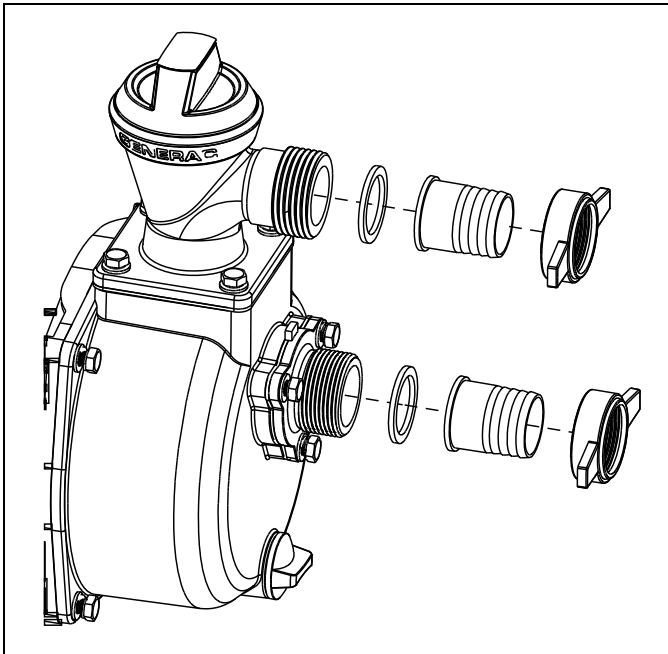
Fixation d'un joint et d'un raccord cannelé
